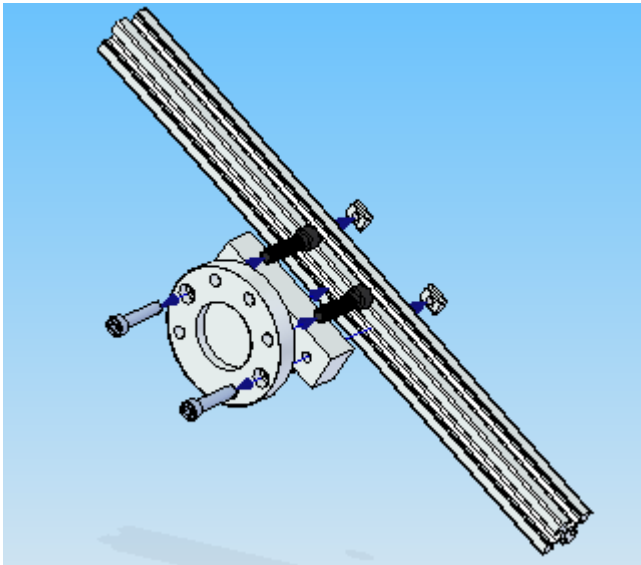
Explosionado del conjunto “Soporte montado”.
